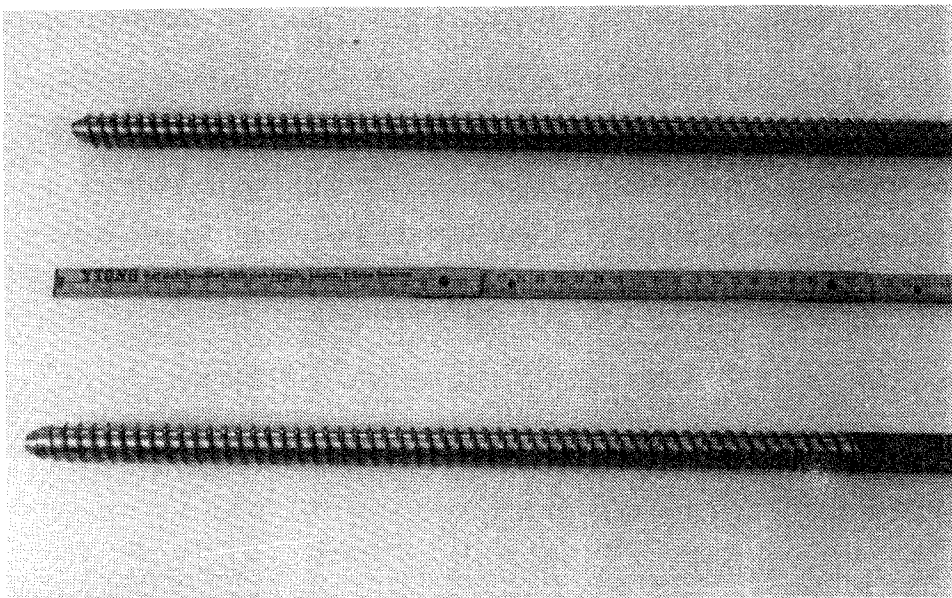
Unregelmäßigkeiten in der Gewindetiefe bei Stangen mit Holzschrauben - Gewinde
